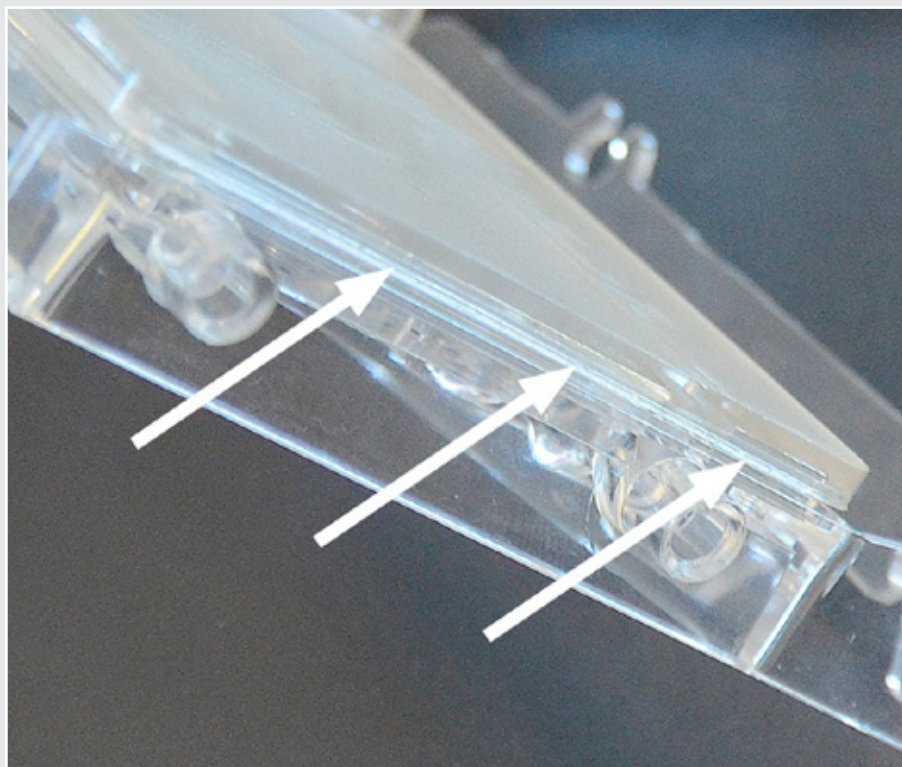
Sauber und dicht geschweisste Fügeebenen.
